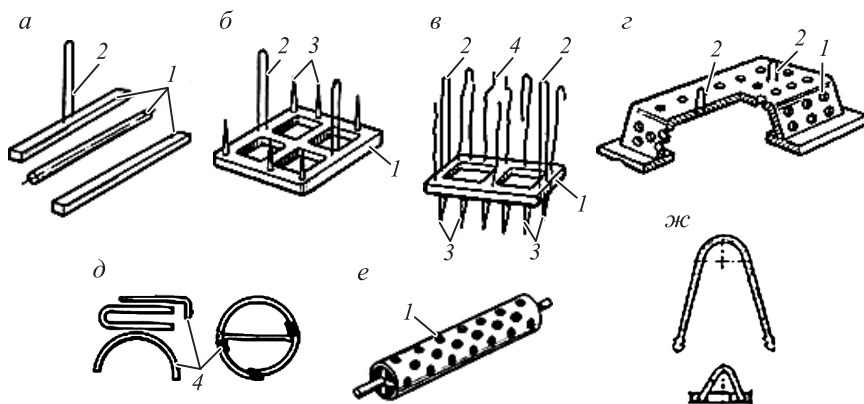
Каркасы стержней и вески для перемещения стержней: а – планочный литой; б – рамочный литой; в – комбинированный; г – коробчатый; д – проволочные; е – трубчатый с вентиляционными отверстиями; жс – вески для проволочных и литых каркасов; 1 – основание; 2 – подъемы; 3 – торцы; 4 – проволока
